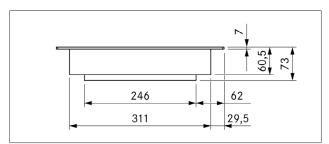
Dimensões do aparelho PKT3, vista dianteira
